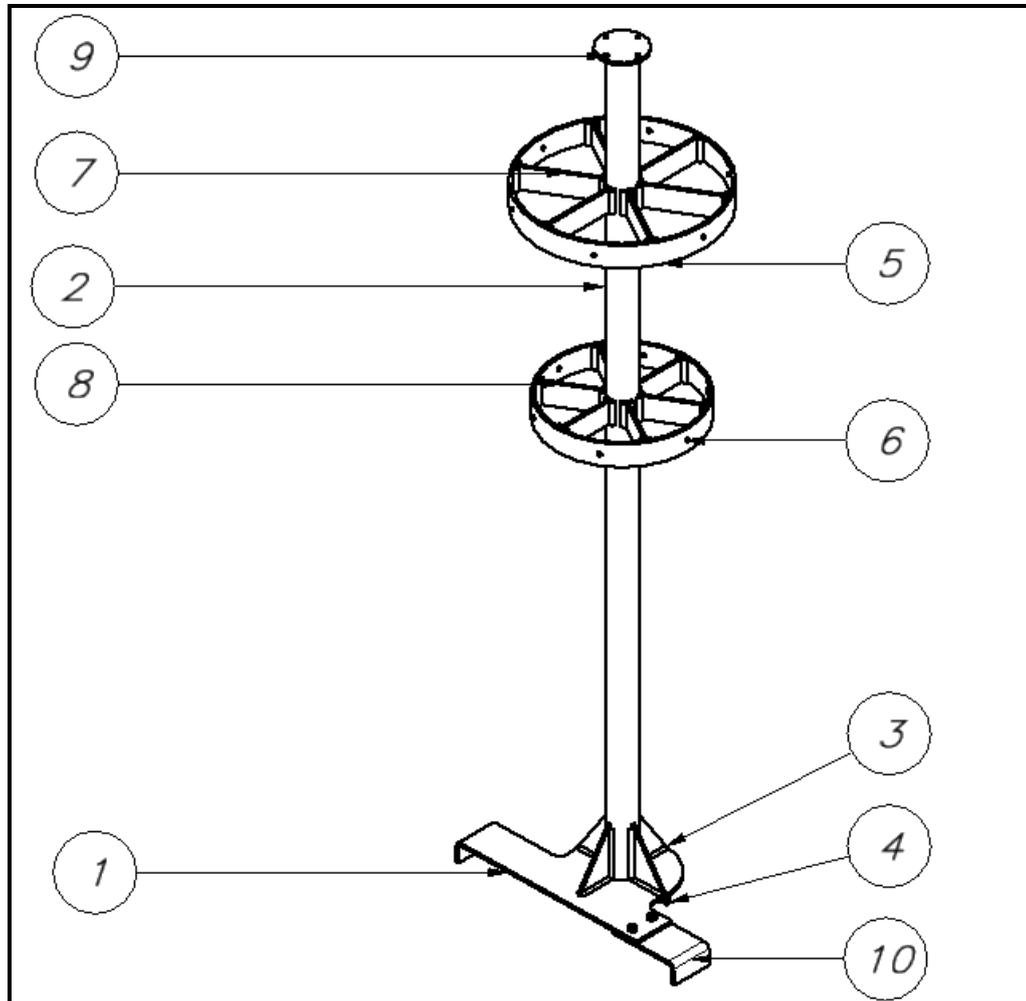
Vista de la Estructura Central (Fuente: Propia)
